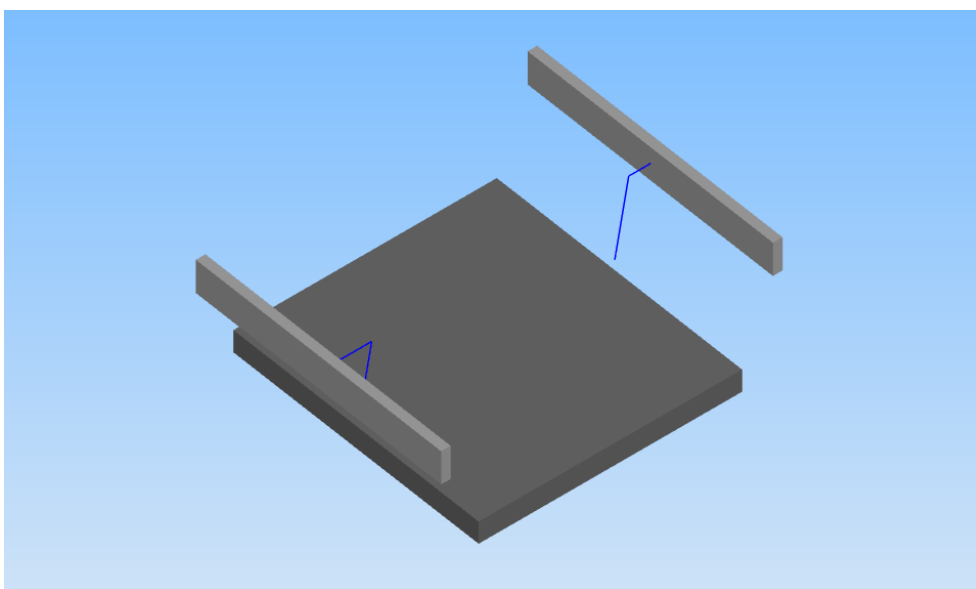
Vista explosionada del ensamble mostrado en la figura 3.22.
